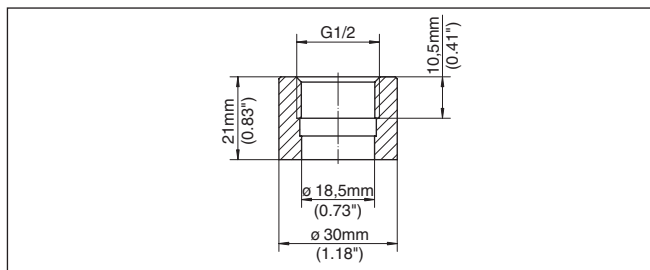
Dimensiones racor para soldar G $\frac{1}{2}$ (ISO 228-1) frontal rasante - VEGA-BAR 82
